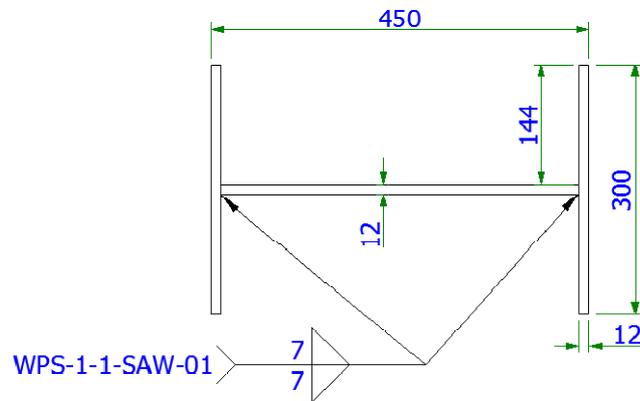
35 Detalle de Soldadura Patines y Alma
